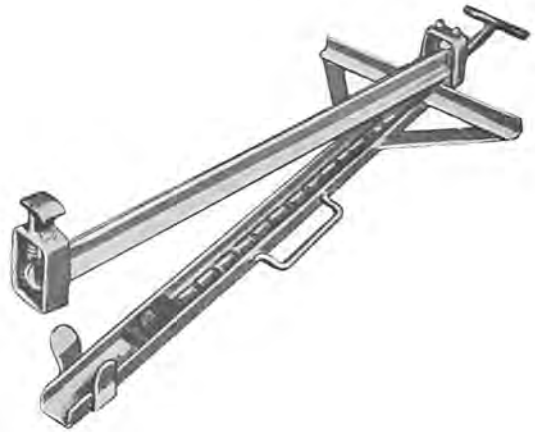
Machine «Comet» à couper les courroies. La bande se place entre la glissière inférieure et la double cornière supérieure.
